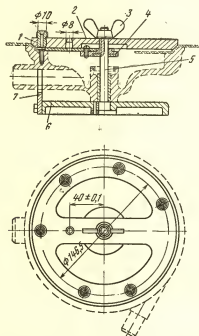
Кондуктор для высверливания сломанных винтов из корпуса насоса стиральной машины «Рига-55»;
